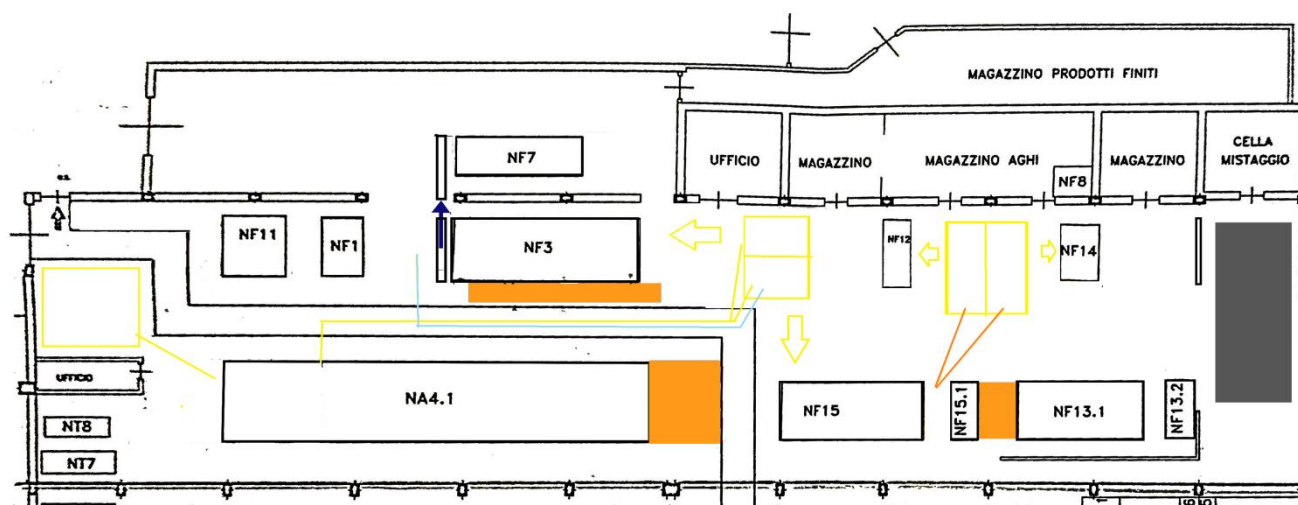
nuovo layout dell'impianto comprendente dei buffer.
